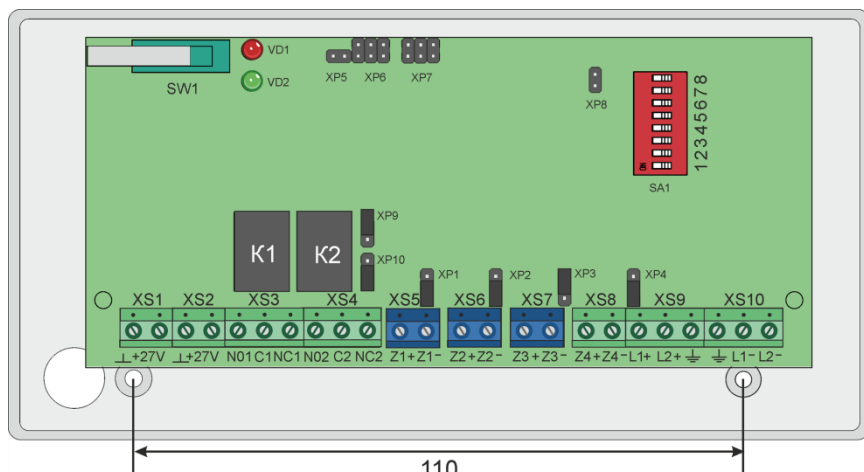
Внешний вид основания корпуса и платы МШ4-2
